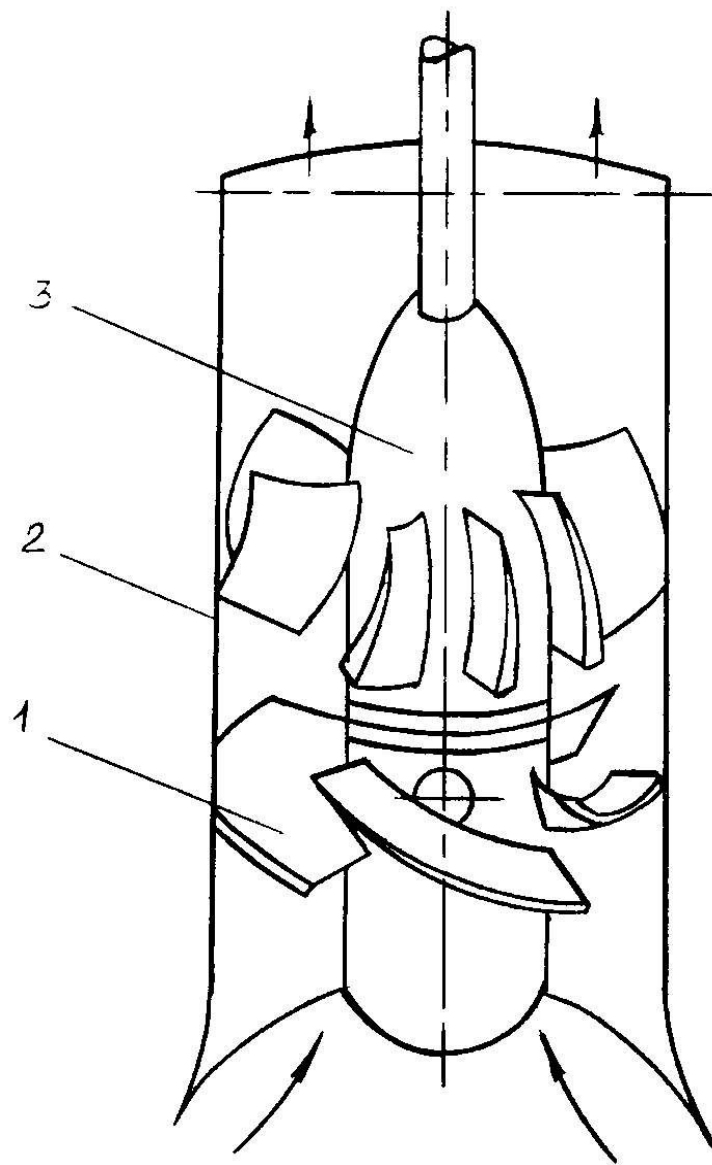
Схема осевого (пропеллерного) насоса: 1 – рабочее колесо; 2 – корпус; 3 – направляющий аппарат;
